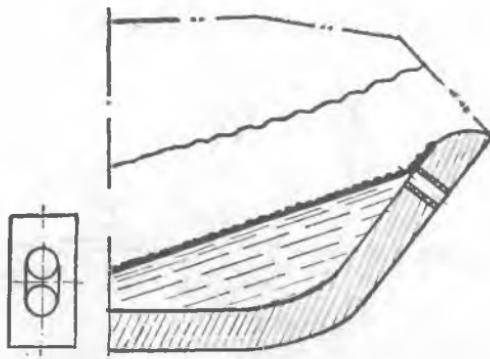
Установка в конвертор графитового стакана для выпуска металла [66].
